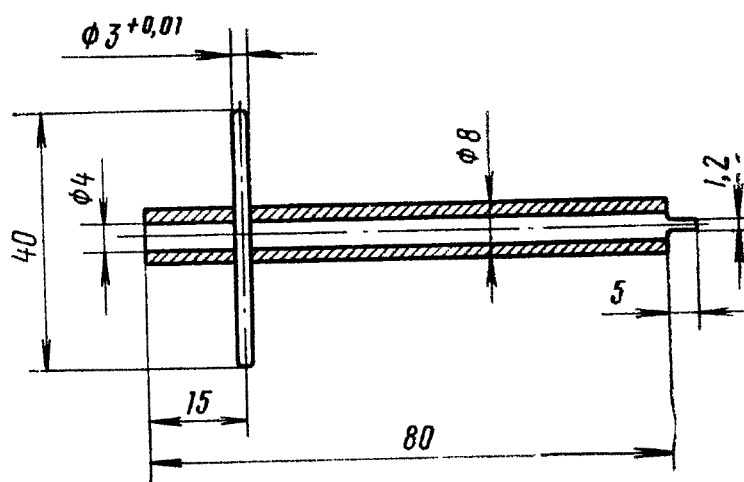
Ключ для разборки корпуса блока электропневматических клапанов
